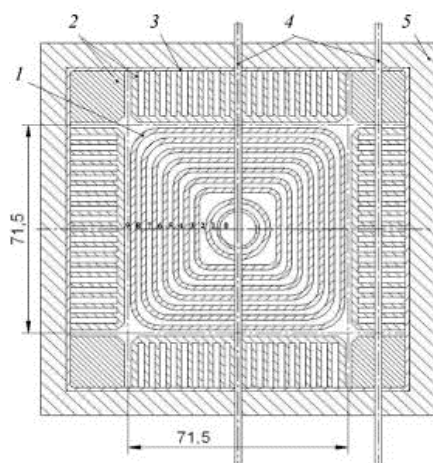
Поперечный разрез колонки гидравлического стенда [1]:
